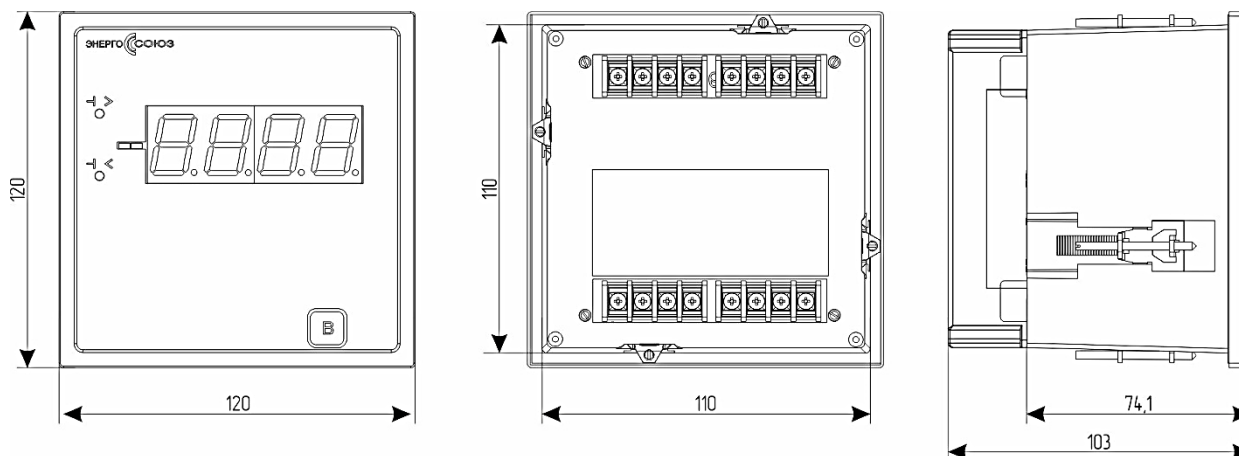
Габаритные и установочные размеры конструктивного исполнения TP
